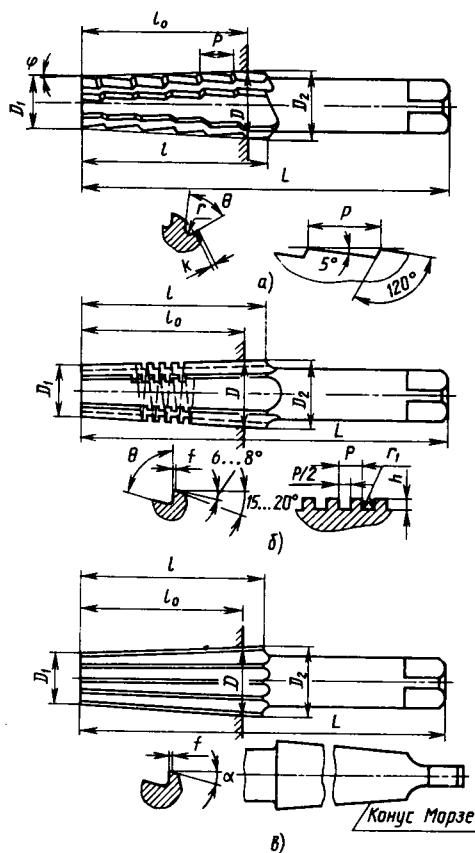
Комплект разверток для обработки отверстий под конуса Морзе и метрические: а — черновая; б — промежуточная; в — чистовая
